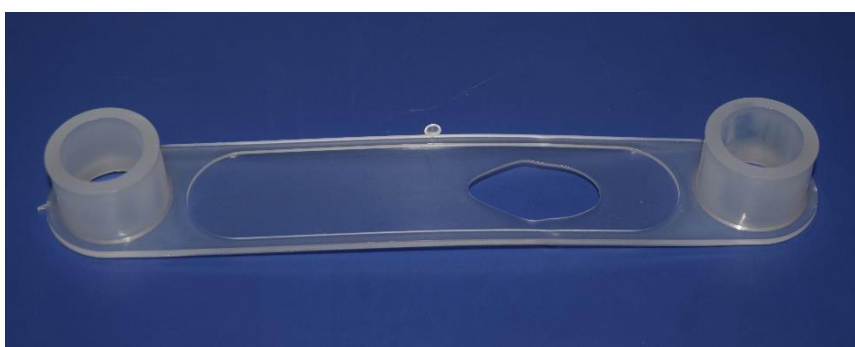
2 Biela fabricada que presenta falta de llenado en su base
